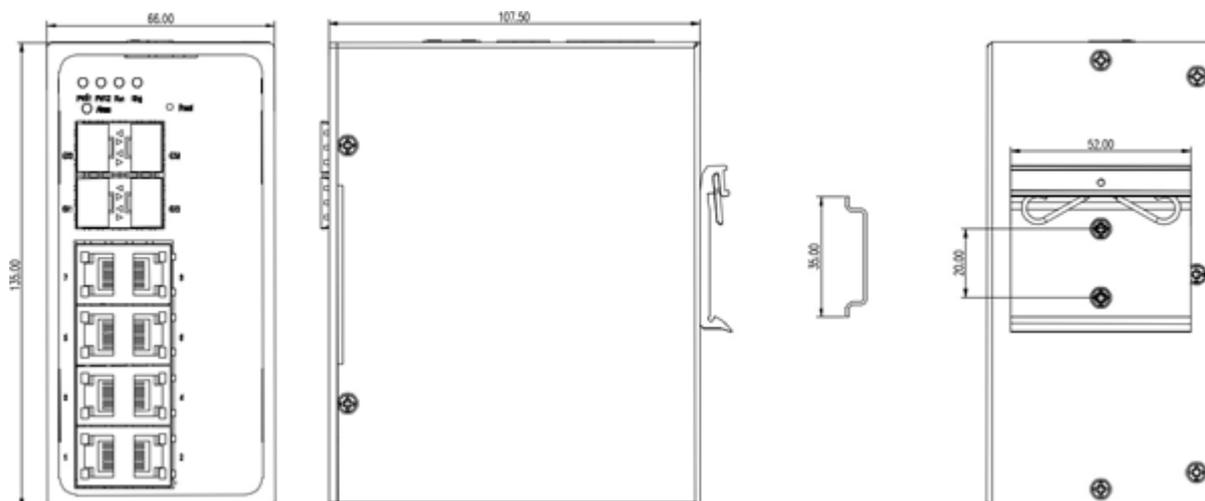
Габаритный чертеж корпуса «Тип 1» с креплением на DIN-рейку
